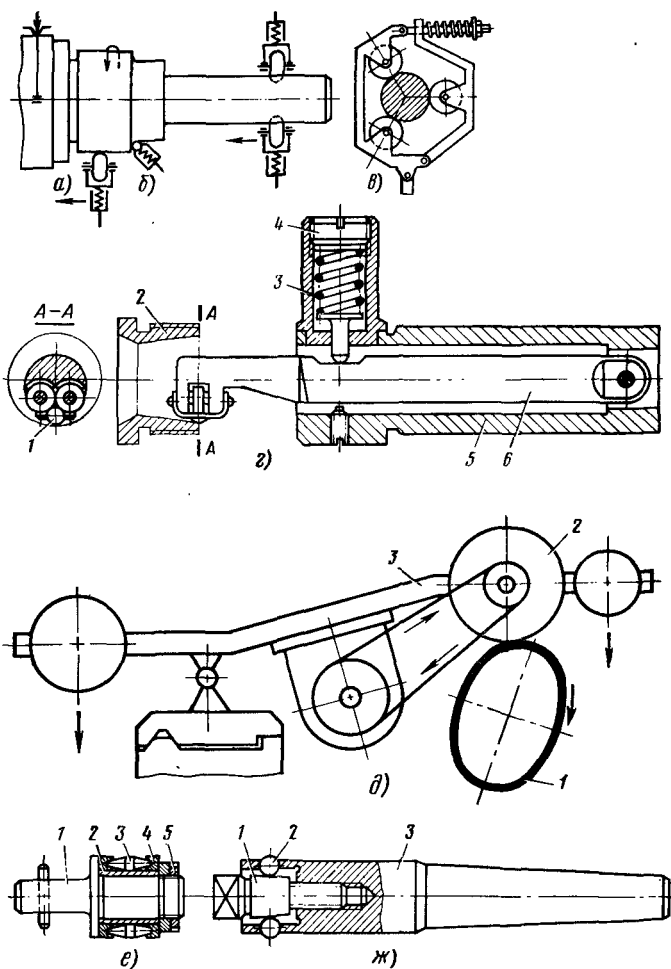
Схемы процесса обкатывания и раскатывания поверхностей вращения:
